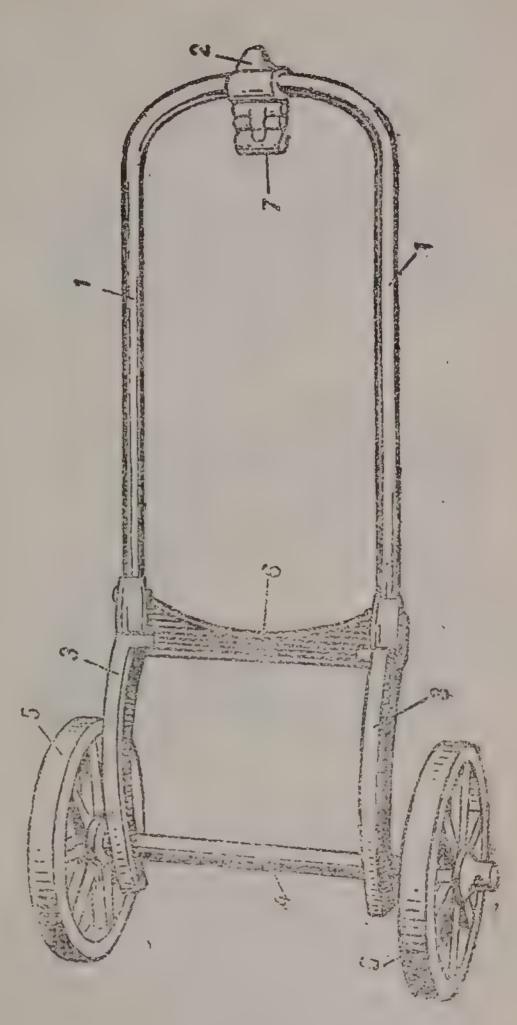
Остов станка: 1 — хобот; 2 — сошник; 3 — дуги; 4 — ось; 5 — колеса (катки); 6 — связь; 7 — серьга
